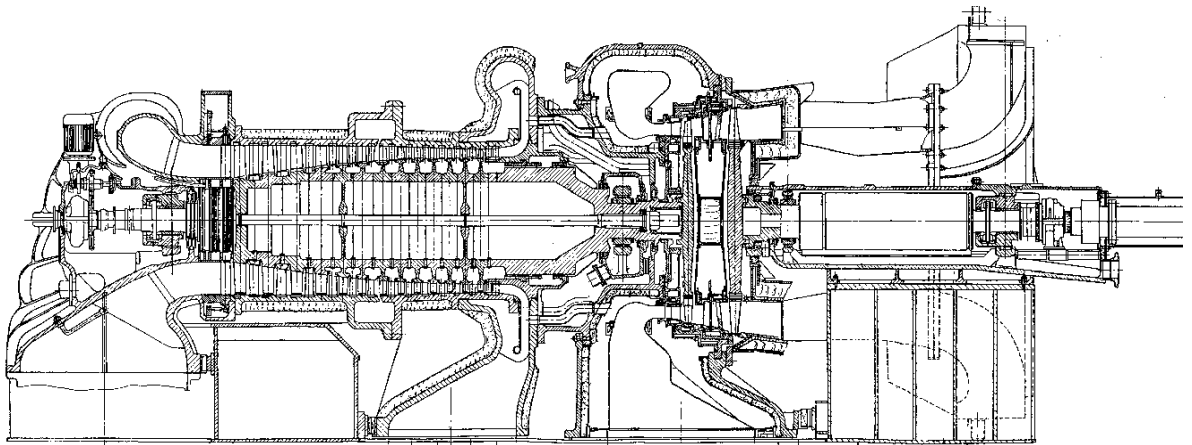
Газотурбинная установка ГТНР-16 («Невский завод») для привода газоперекачивающего агрегата
